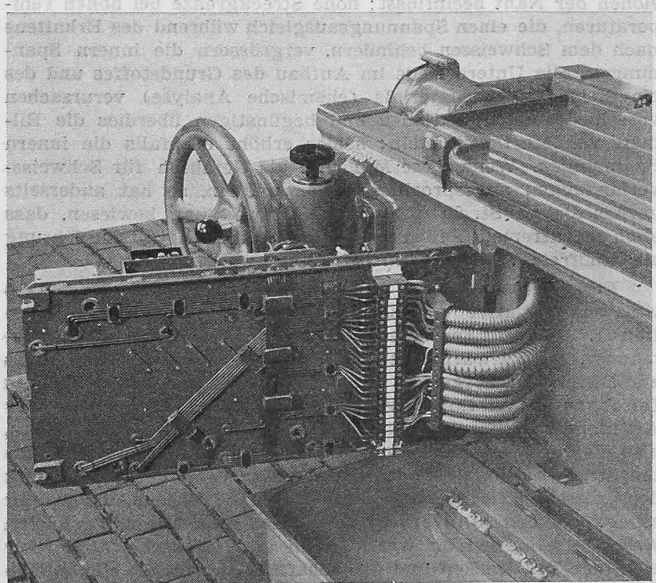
Aufgeklappter Steuerkasten mit leicht zugänglichen Kabelanschlüssen
